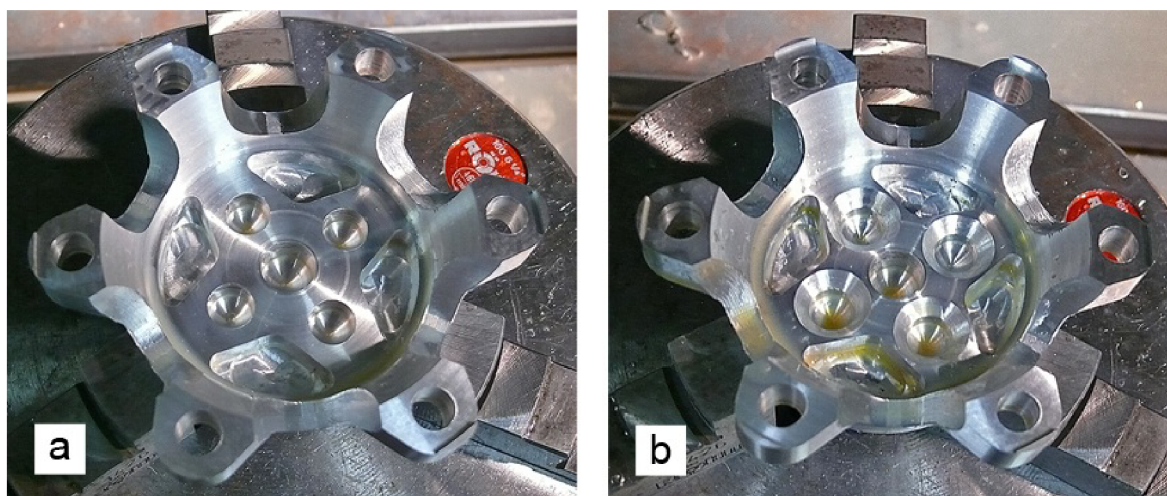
Stav obrobku po a) hrubování kapes, b) zbytkovém dokončení kapes.
